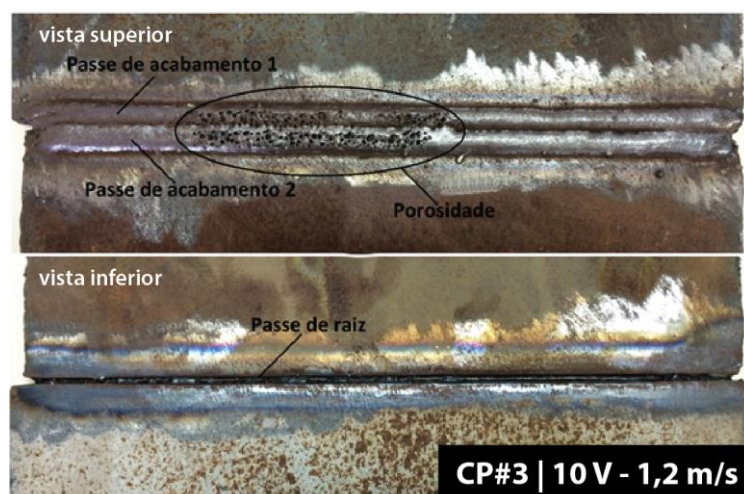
Cordões de solda realizados no corpo de prova 3 (CP#3).
